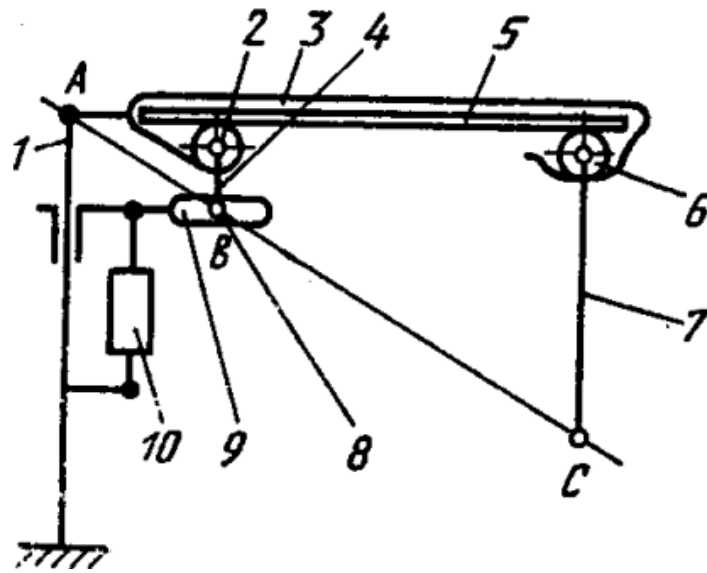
Схема збалансованого маніпулятора із зубчато-рейковим механізмом: 1 – стійка; 2 – зубчасте колесо; 3 – порожній важіль; 5 – зубчаста рейка; 6 – зубчасте колесо; 7 – вертикальний важіль; 8 – вісь ролика; 9 – горизонтальна куліса каретки; 10 – привод лінійного переміщення.
